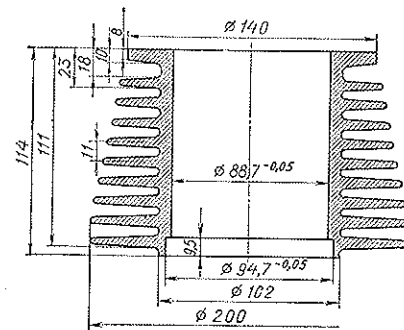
Рубашка цилиндра двигателя Д-3А.
